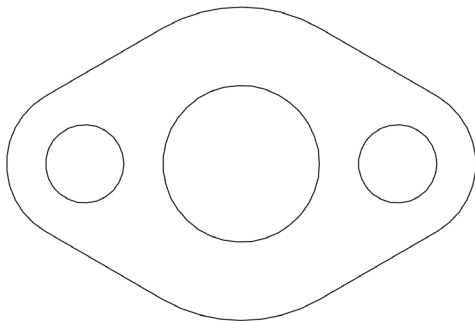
Die CAD-Zeichnung einer Stopfbüchsenbrille
